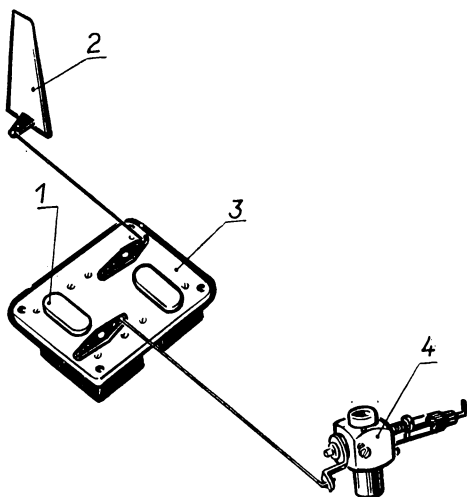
Схема управления рулем поворота и оборотами двигателя:
